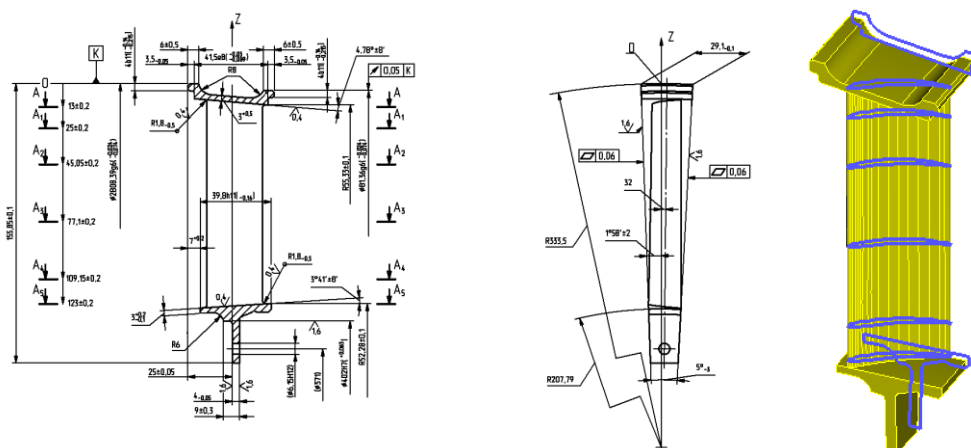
Чертеж и модель двухполочной лопатки
